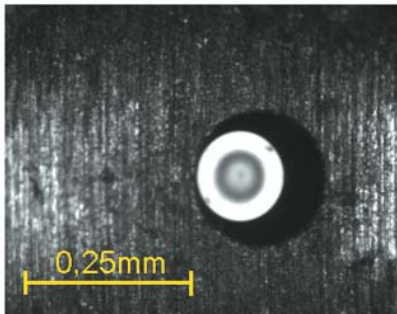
Fasertaster im Eigenleuchtmodus (Messung einer Einspritzdüse, Eintauchtiefe 0 mm)
